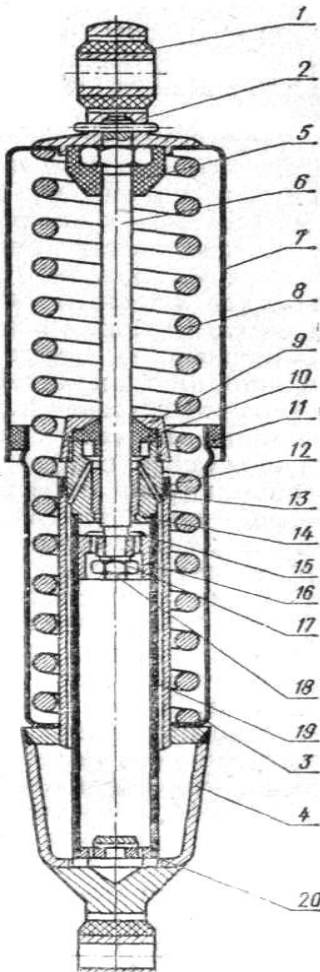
Пружинно-гідролічний амортизатор задньої підвіски:
